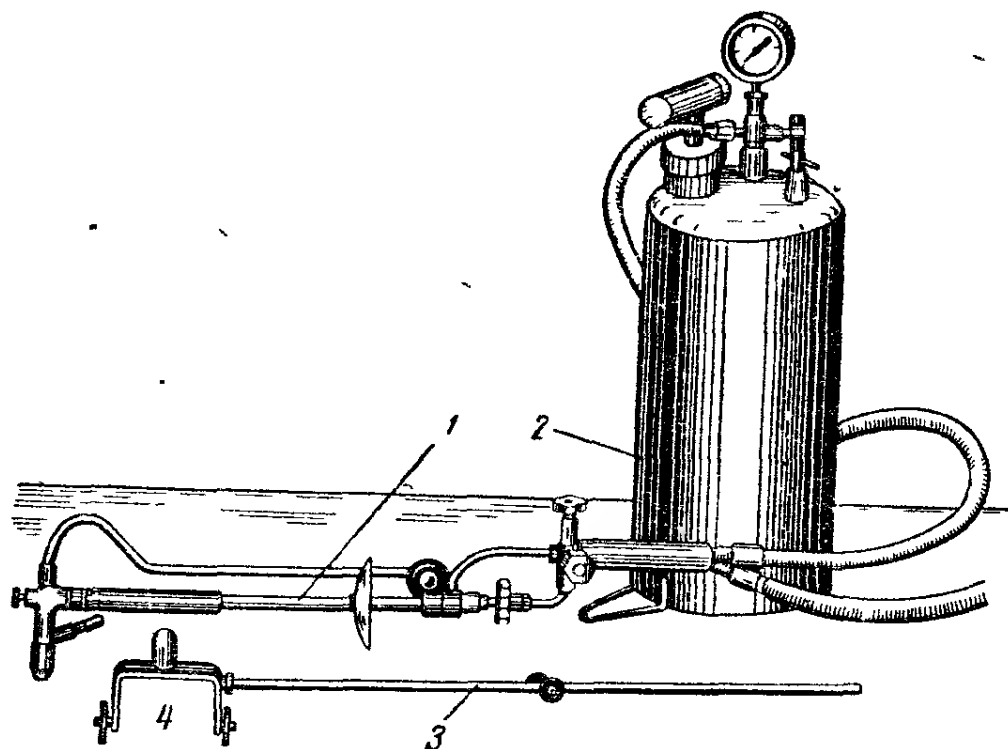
Внешний вид керосинореза К-51 и бачка для керосина:
